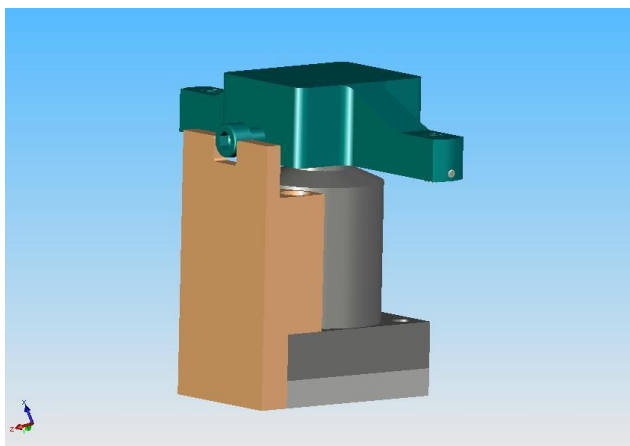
Conjunto cilindro e garra basculante para aperto do braço de direcção (Cilindro Central)
